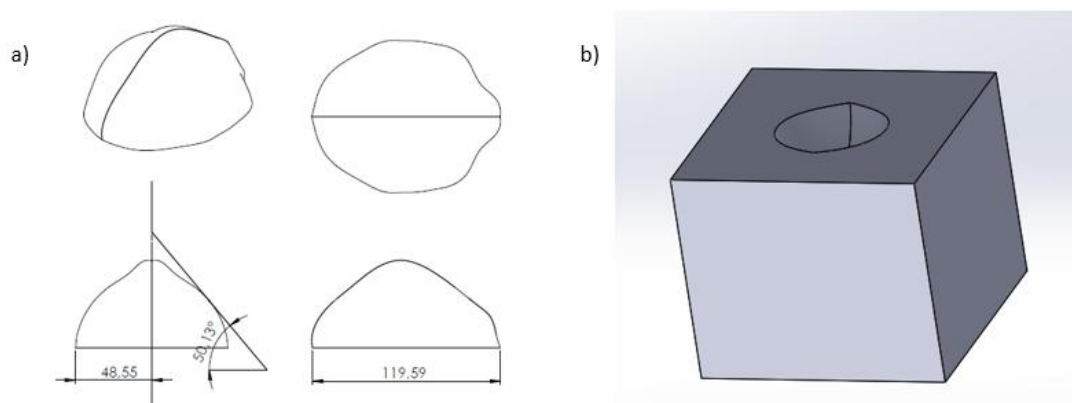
a) Desenho técnico da calota craniana; b) molde utilizado no EdgeCam.
